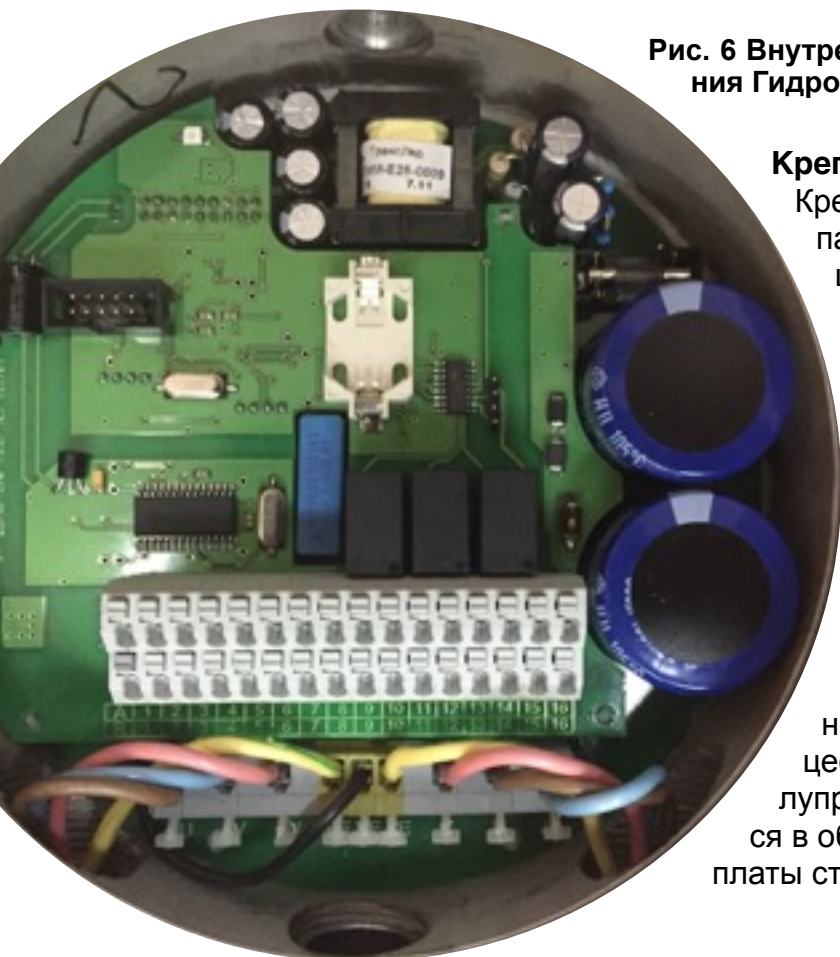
Внутреннее устройство взрывобезопасного исполнения Гидроматик-101 8го поколения типоразмер корпуса 1
